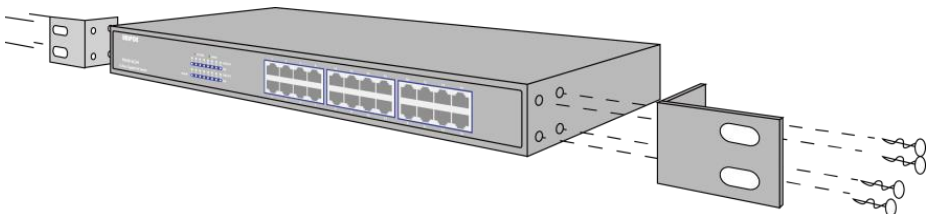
Установка боковых креплений на коммутатор SW-8160/TB
